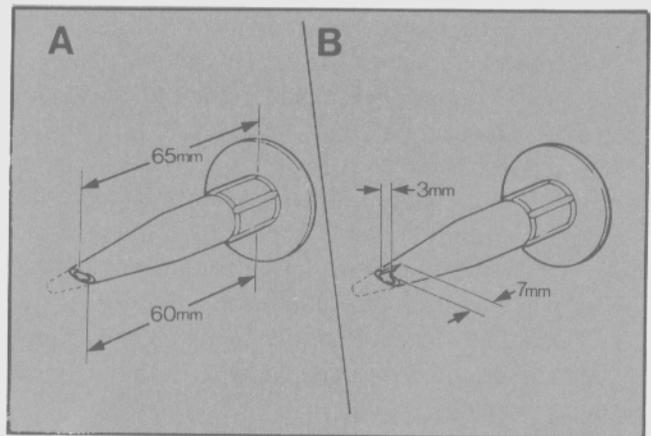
Cortes a realizar en la boquilla aplicadora de adhesivo.
